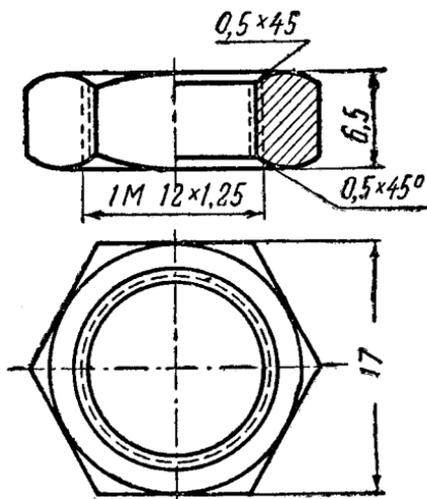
Дет. № 356. Гайка к крышке поплавковой камеры
